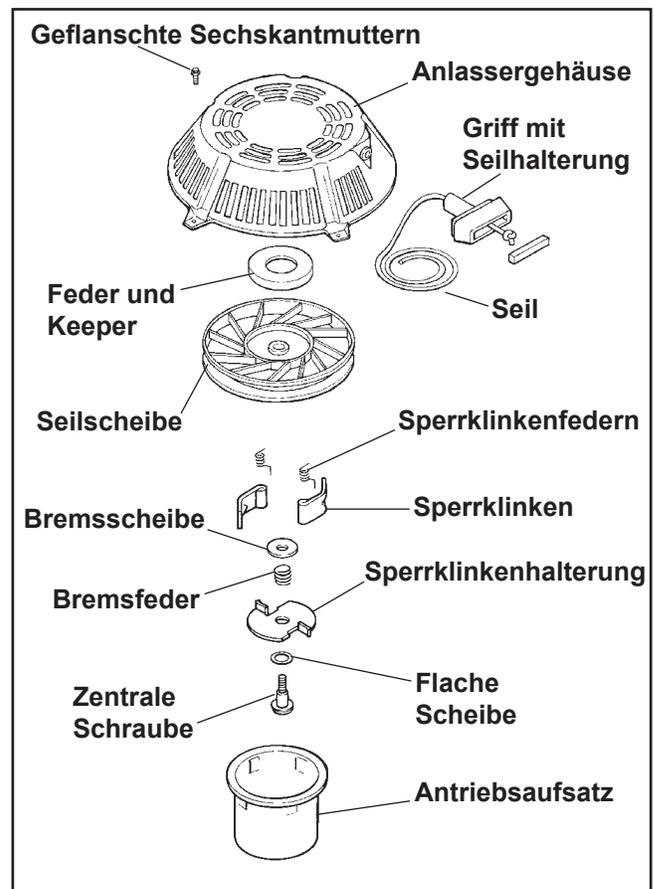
Seilzuganlasser - Explosionsansicht.
